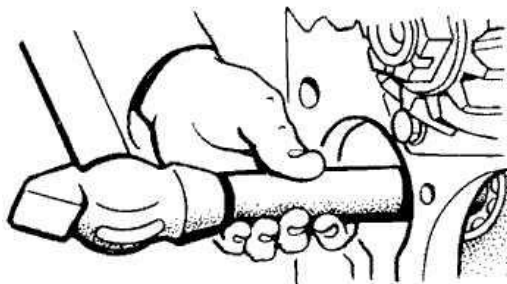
Выпрессовка вала 1-й передачи и заднего хода
